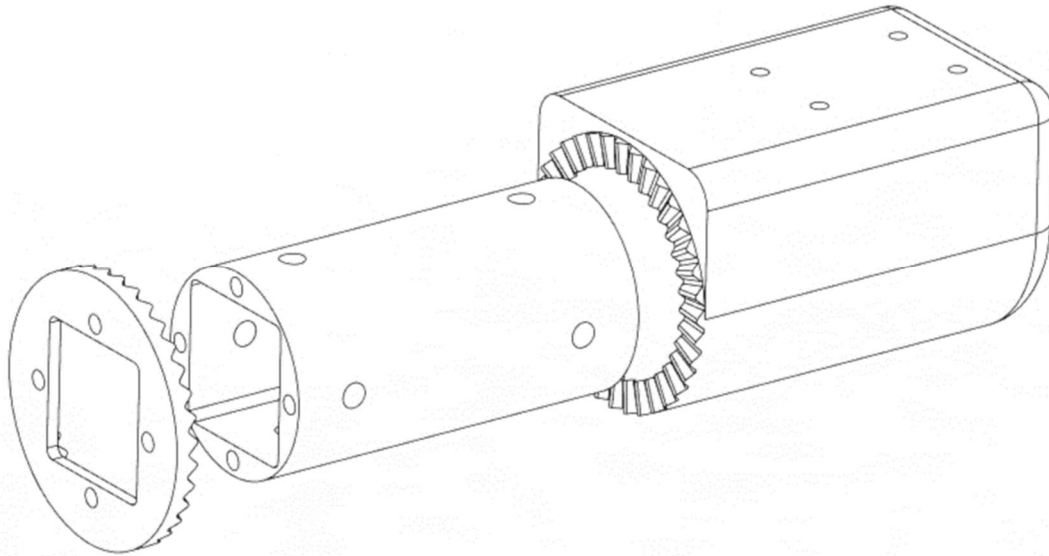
Componentes do módulo rotativo e encaixe dos dois módulos (excluindo o motor).
